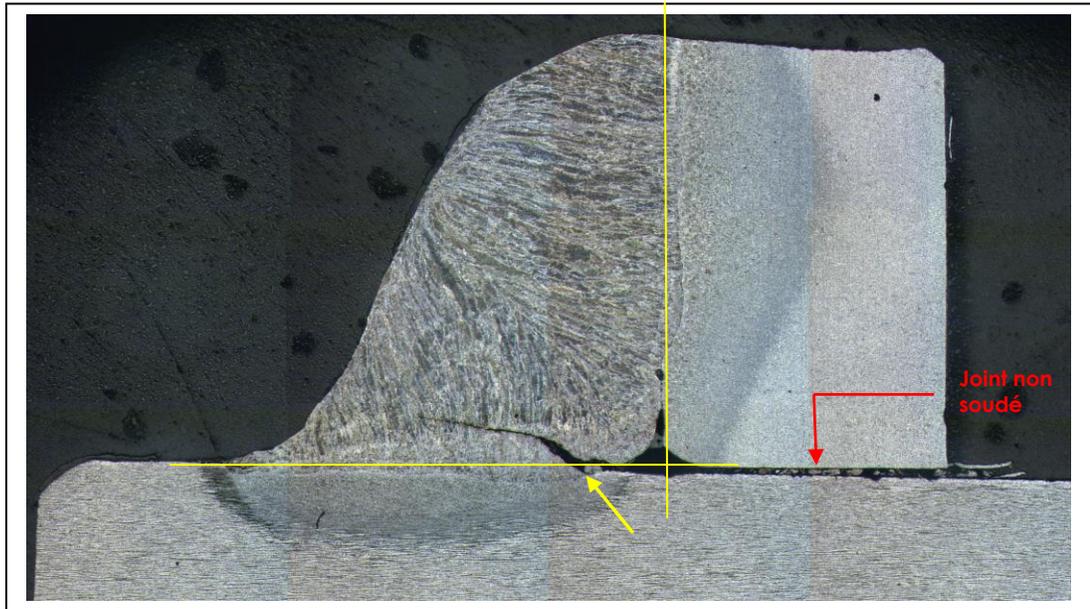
Fissure à la racine du cordon de soudure 1GE - surface int.
